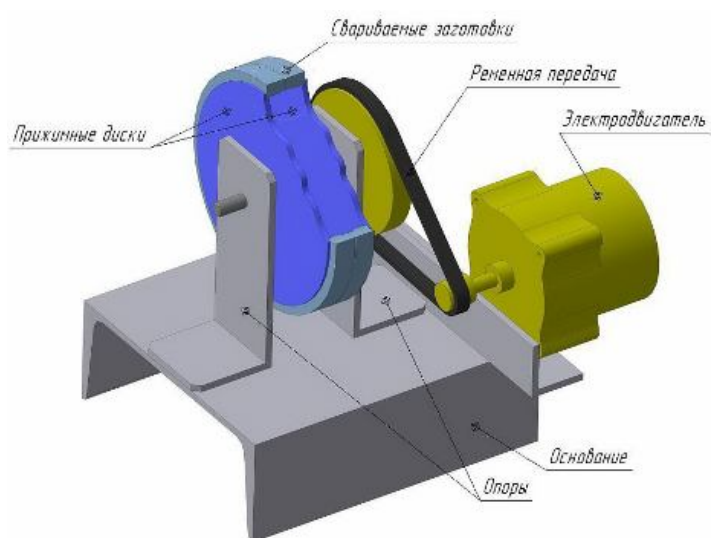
Принципиальная схема оснастки для сварки образцов
